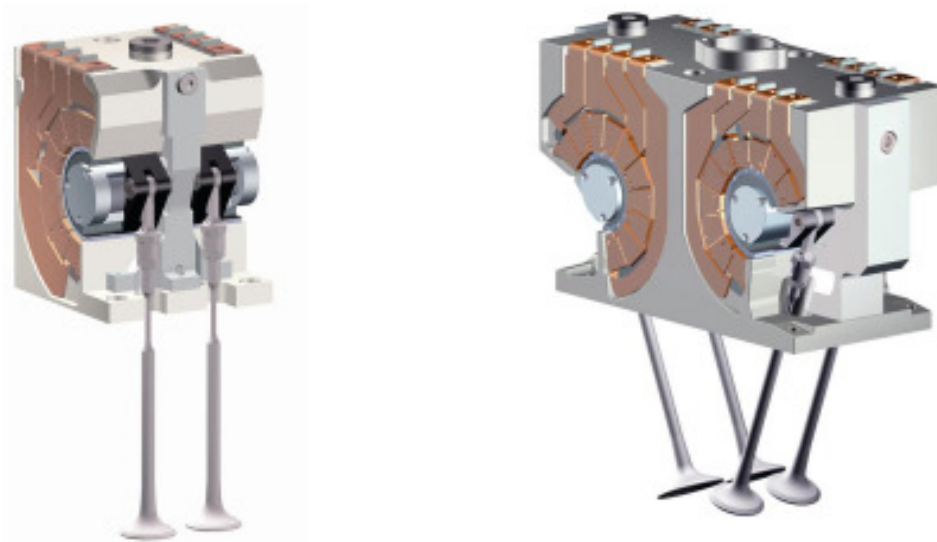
RVT-Aktoren für Otto- und Dieselmotor
